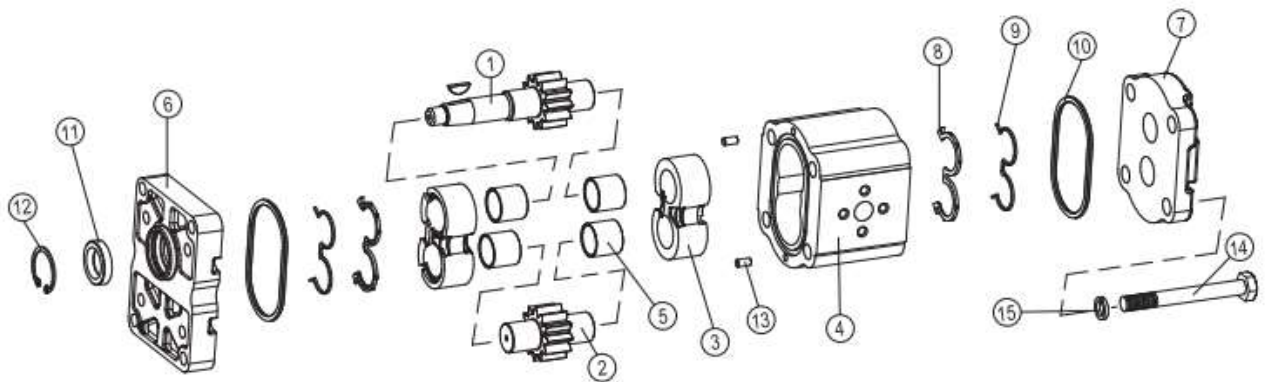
Деталі шестеренного насоса серії GPK: 1 – шестерня ведуча; 2 – шестерня ведена; 3 – корпус підшипника; 4 – корпус; 5 – металофторопластовий підшипник; 6 – монтажний фланець; 7 – кришка задня; 8 – манжета торцевого ущільнення; 9 – пластина захисна; 10 – кільце ущільнювача; 11 – манжета ущільнення валу; 12 – кільце стопорне; 13 – штифт; 14 – болт; 15 – шайба
